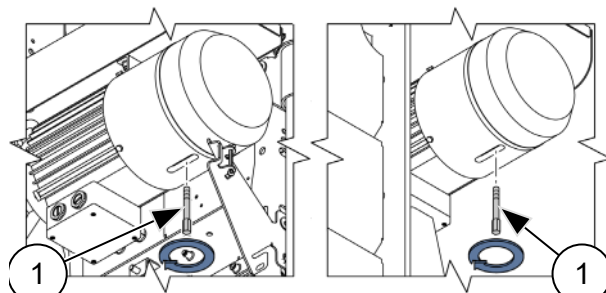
Bremslufthebel in die Motorbremse einschrauben
